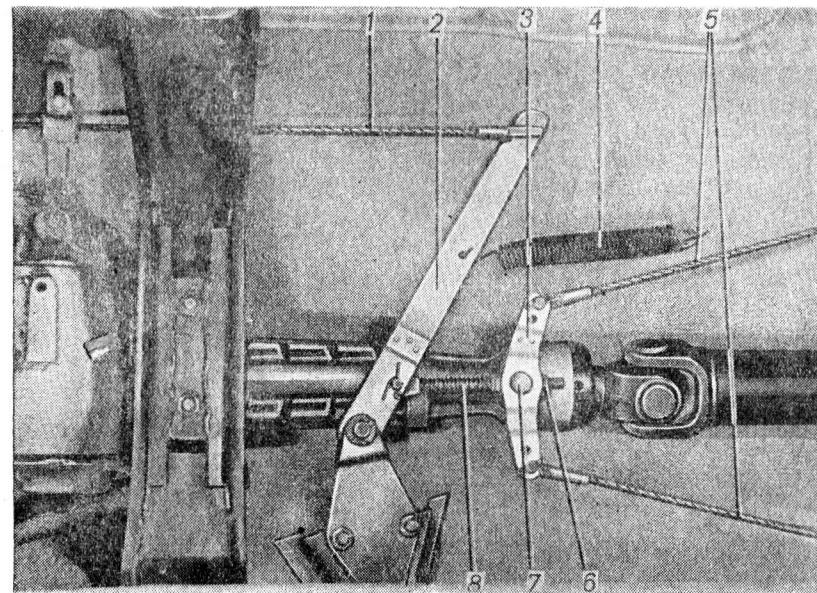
Регулировочный узел механического привода ручного тормоза:
